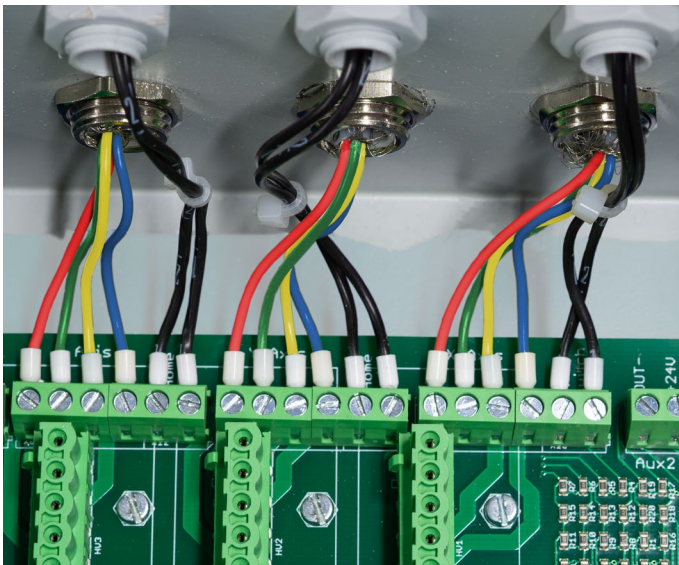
Angeschlossene Kabel für Schrittmotoren und Endschalter
